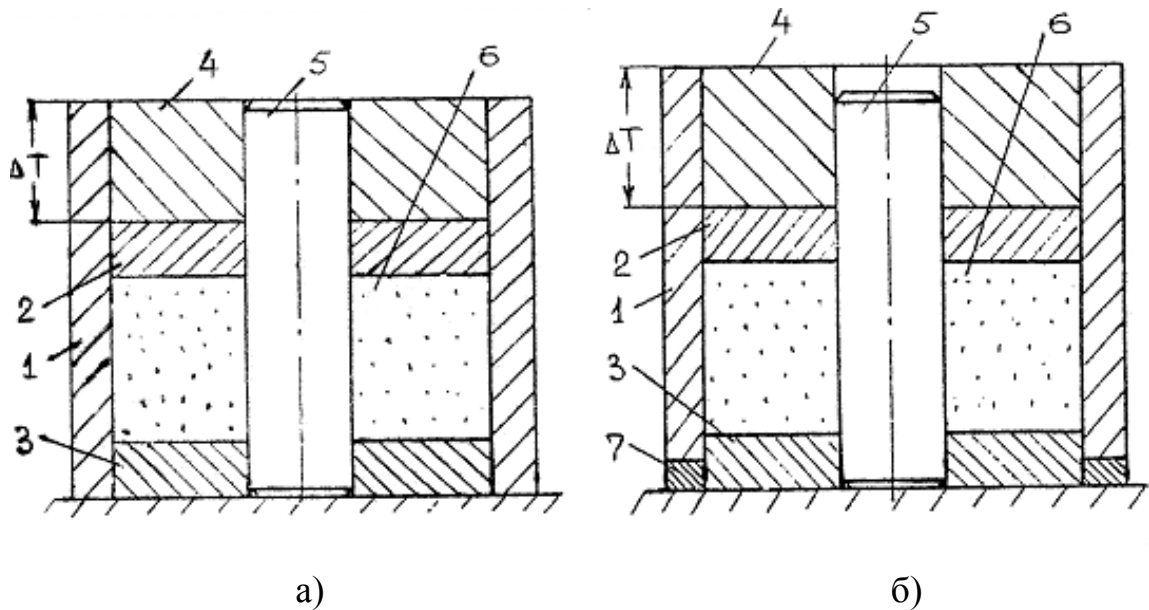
Схемы способов одностороннего прессования в пресс-формах с неподвижными матрицами и с заданными обжатиями:
